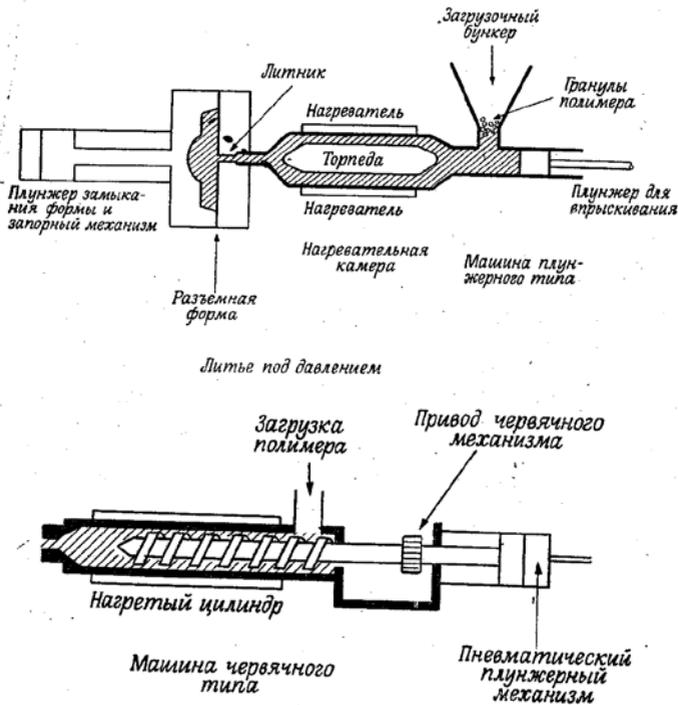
Схема изготовления изделий из термопластов литьем под давлением
